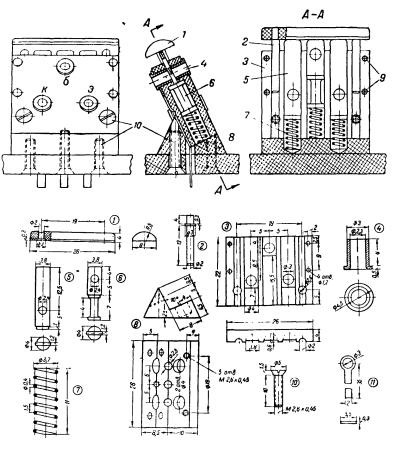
Общий вид и детали пружинного патрона испытателя транзисторов.
